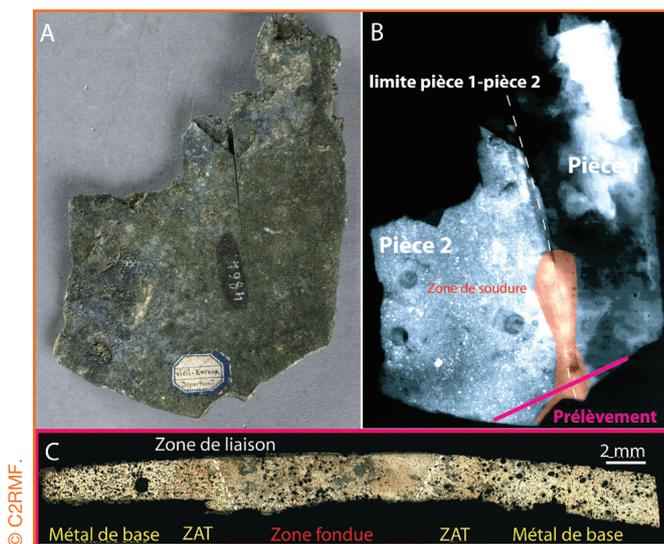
Fragment de statue équestre du Vieil-Évreux constituée de deux pièces soudées.
